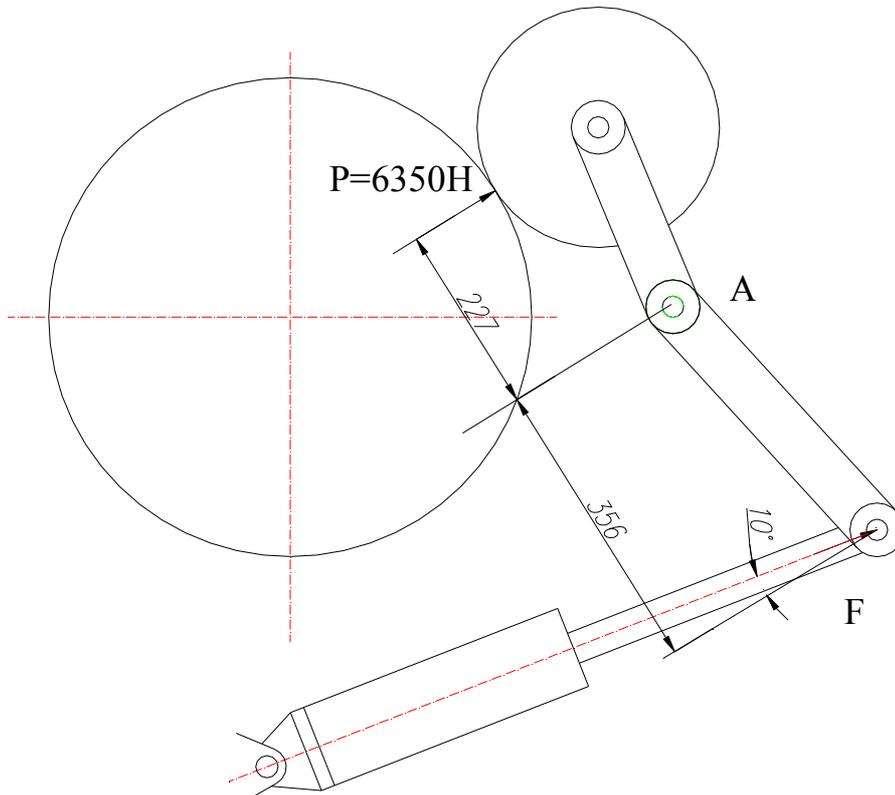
Расчетная схема определения необходимого усилия создаваемого пневмоцилиндром
